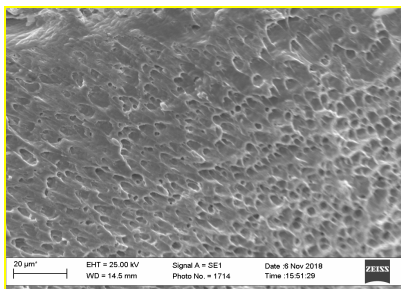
Поверхня зламу зразка по плакованому шару міді.
